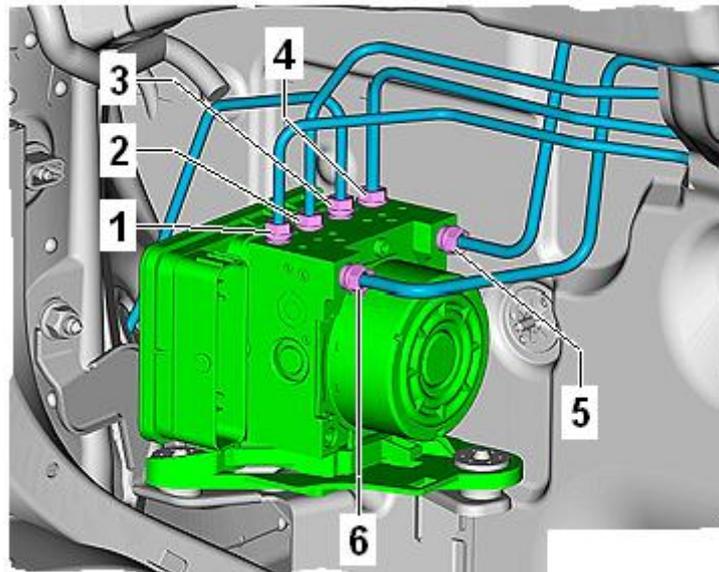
Vue d'ensemble des emplacements de montage du frein avant et arrière.
